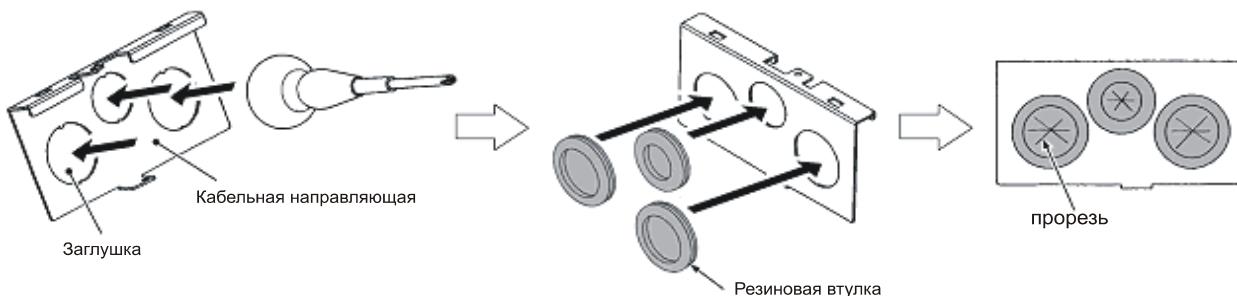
Удаление заглушек из отверстий и установка резиновых втулок
